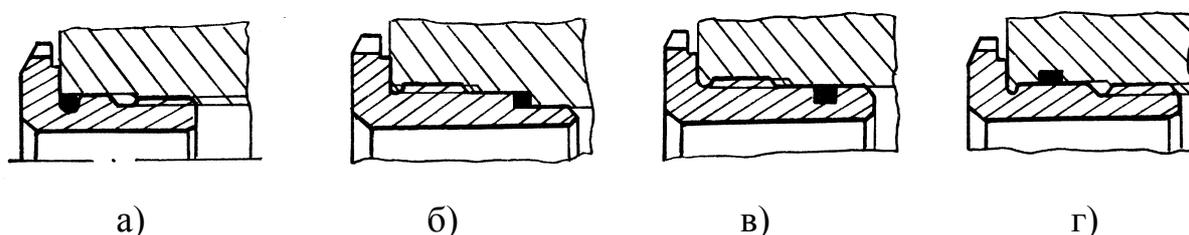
Способы уплотнения резьбовых соединений кольцевыми прокладками и шнурами
